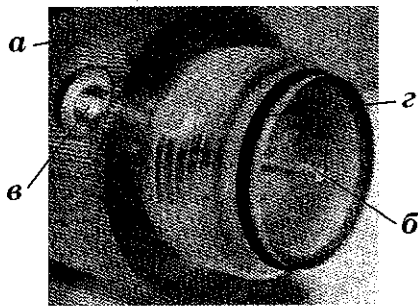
Крышка: а – корпус крышки с отверстиями; б – рабочий канал; в – выпускной канал; г – кольцо резиновое 35-40-30.
